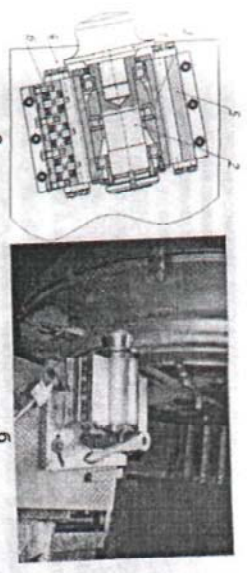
Конструкція розкочувальної головки (а) і загальний вигляд розкочувальної приставки до лобового токарного верстата. 5 – утримувач; 1 – валок; 2 – вісь; 3 – втулка; 4 – спурт верстата; 6 – пружина
